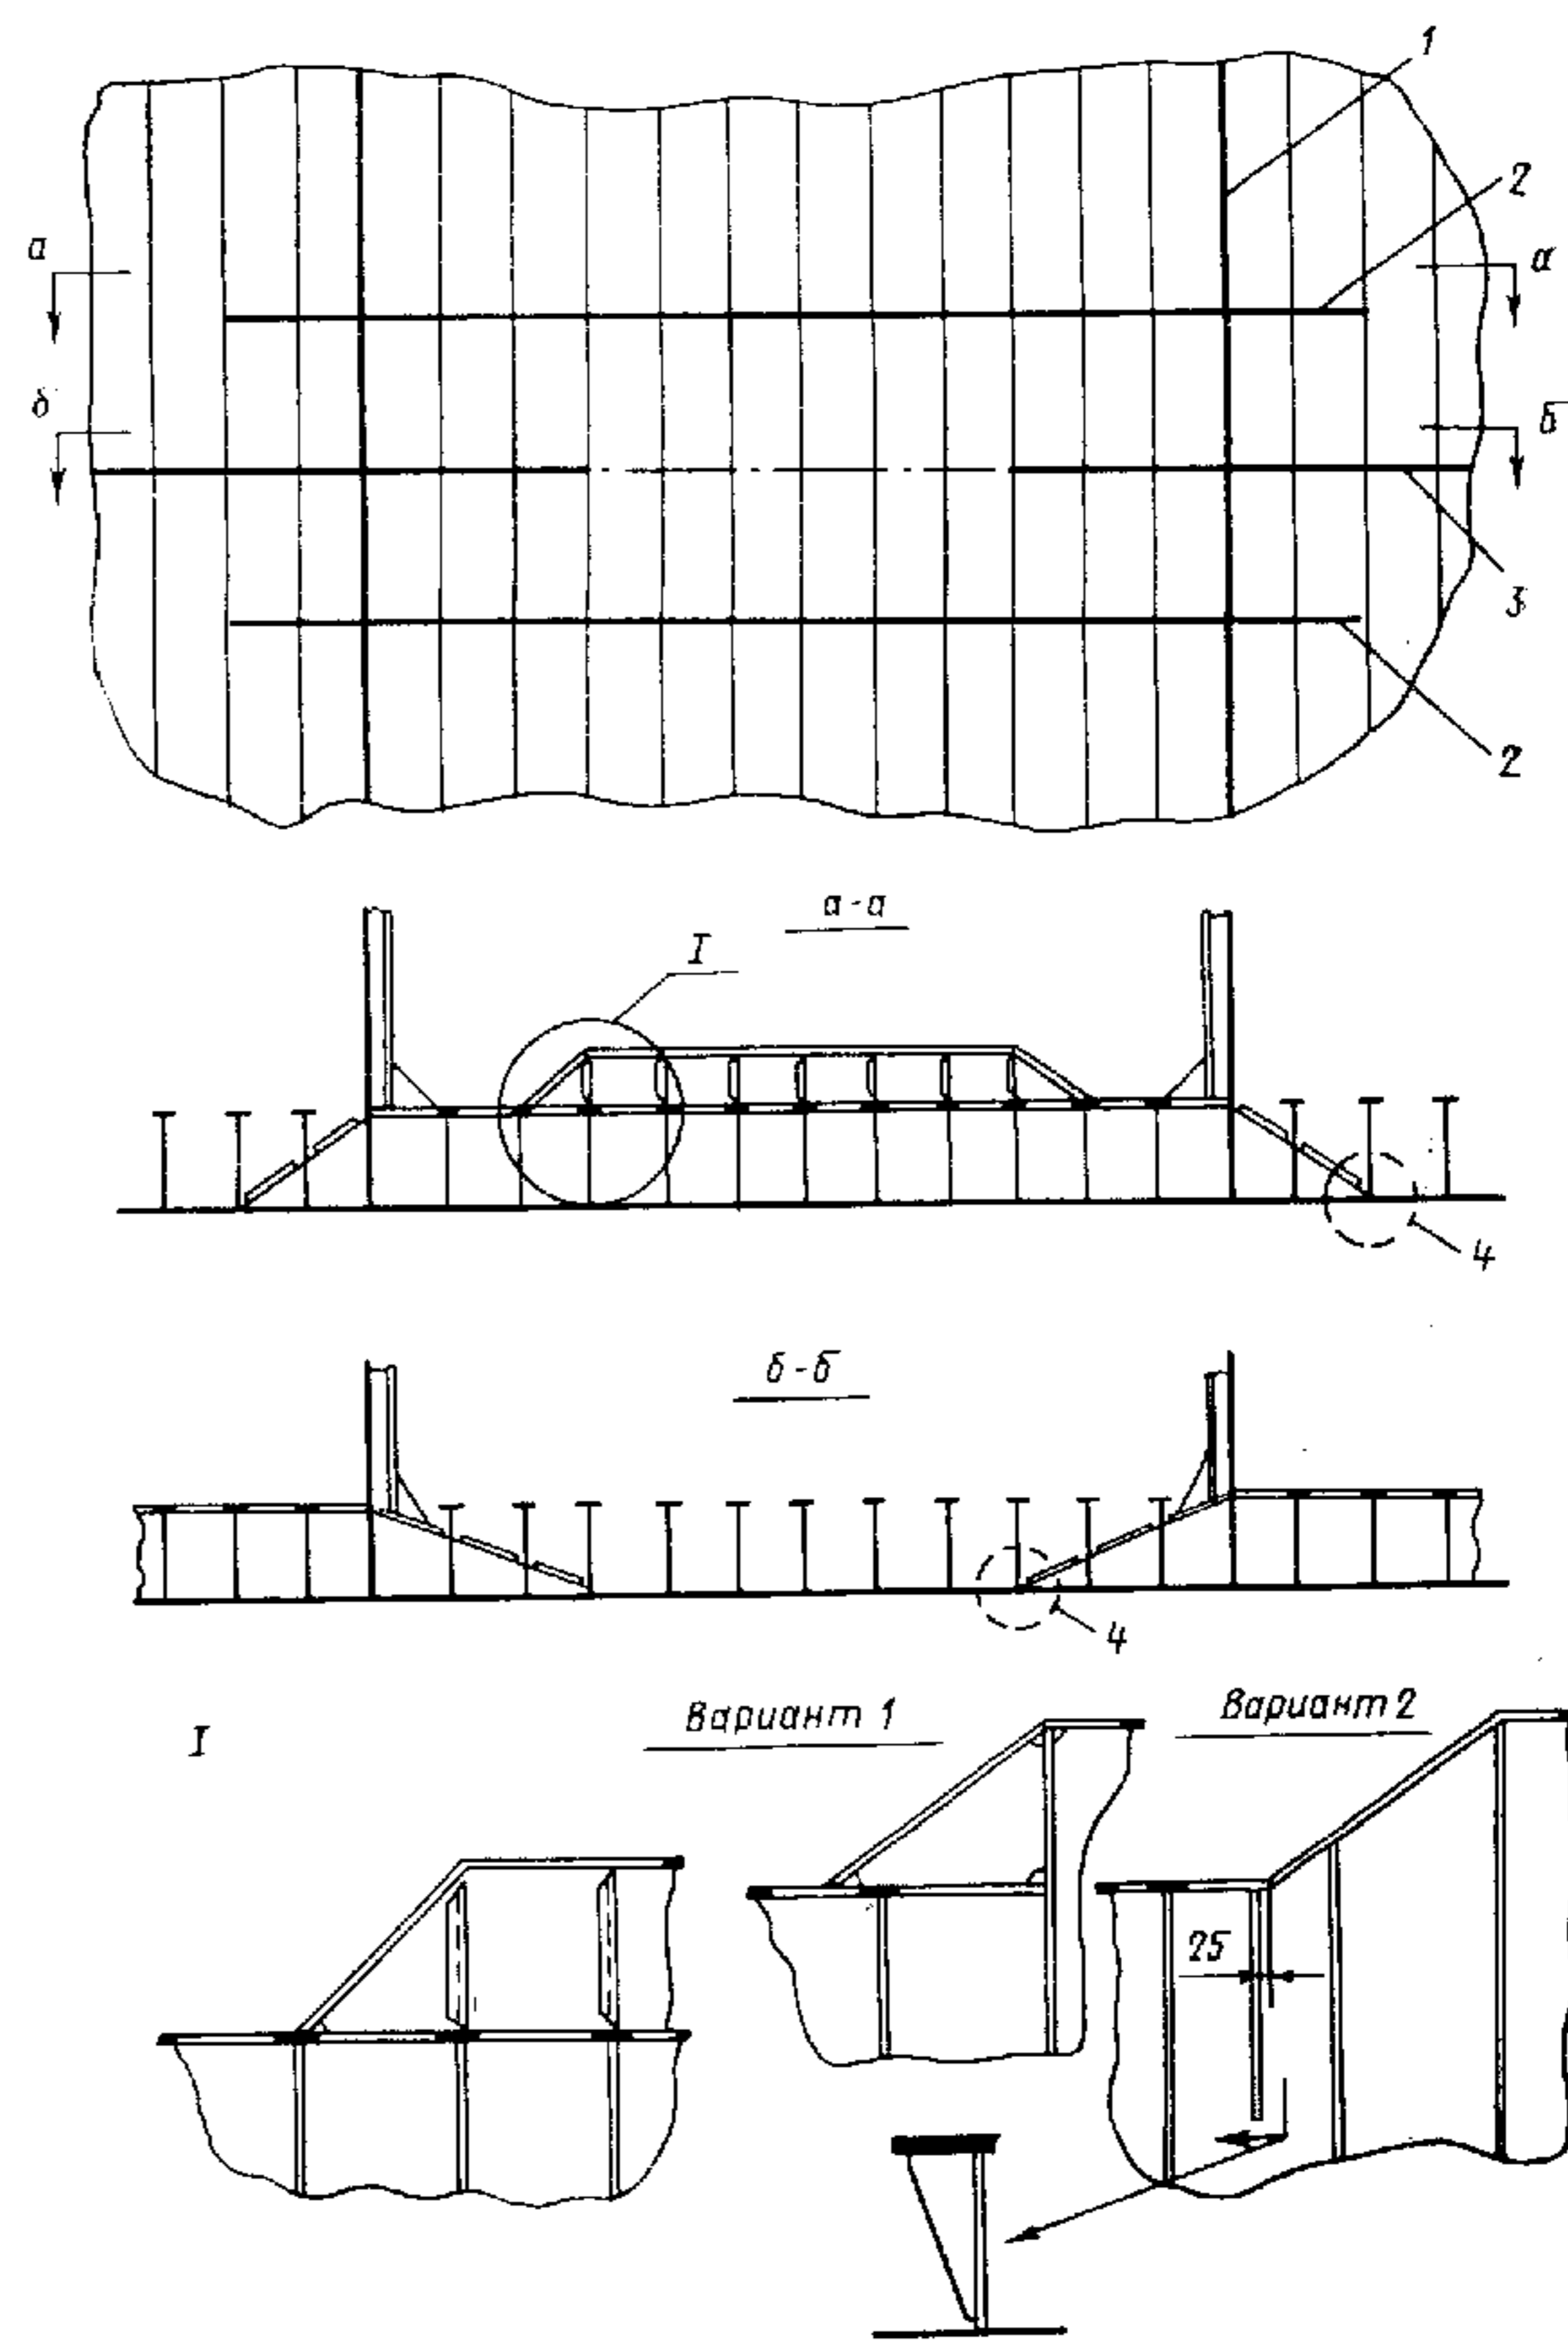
Перевязка продольных балок машинного фундамента и вертикального килья:
